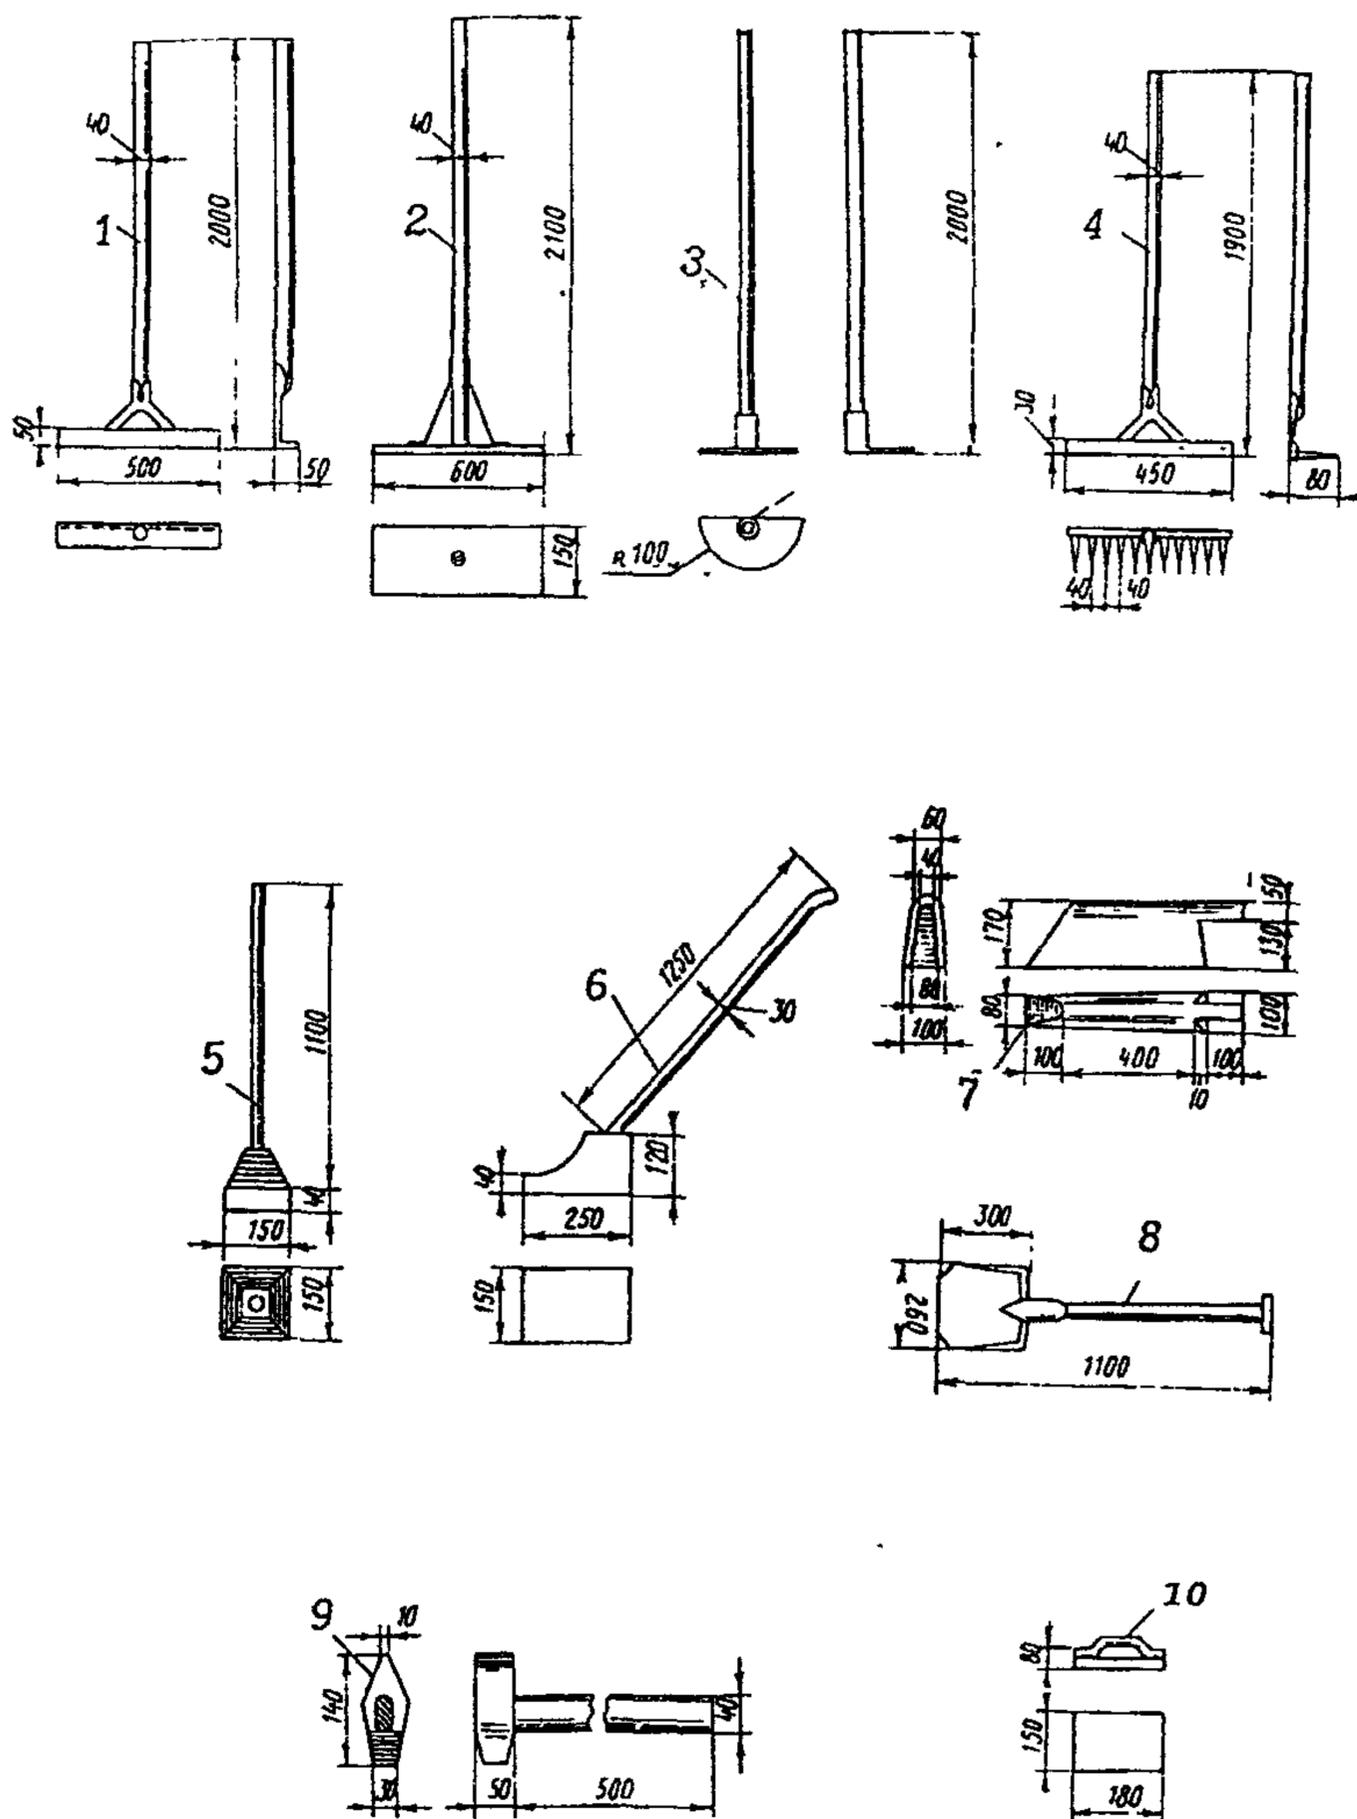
Инструменты для укладки литой асфальтобетонной смеси
